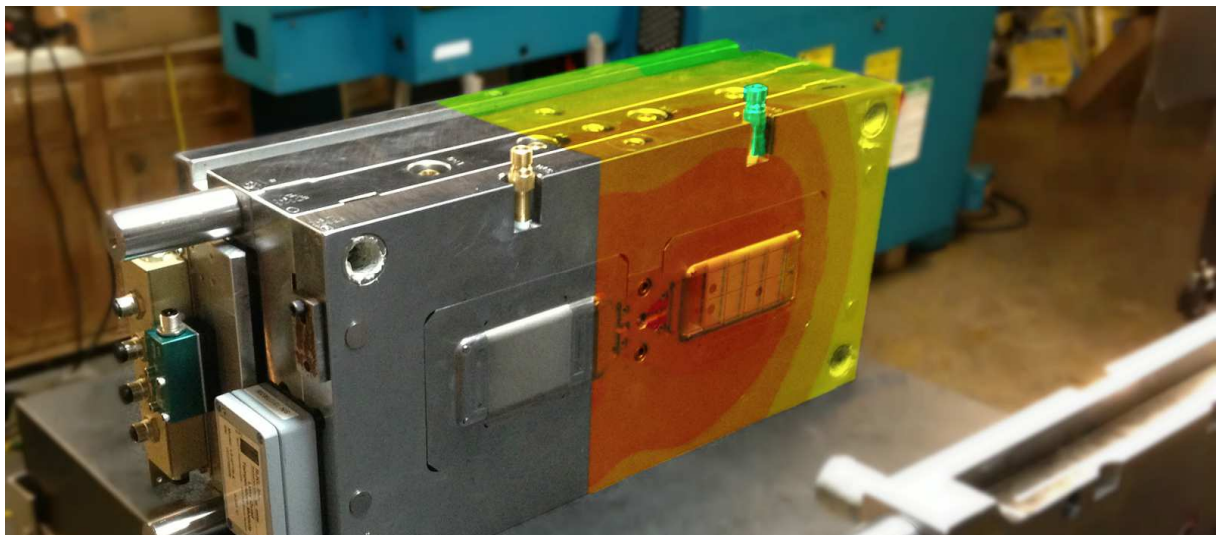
SIGMASOFT® Virtual Molding puede predecir cómo se va a comportar el molde durante la producción. Es posible hacer ensayos de molde teniendo apenas el diseño CAD.
